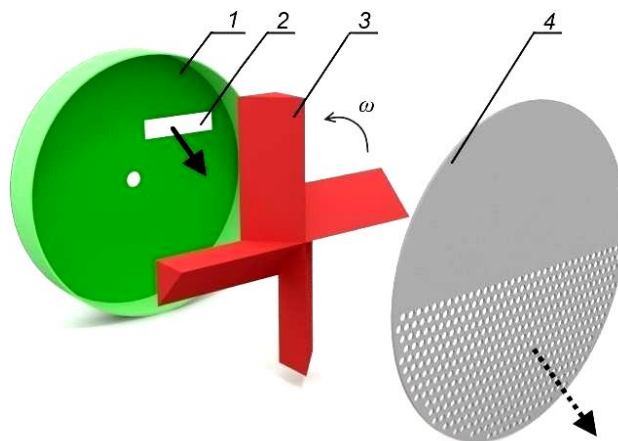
Схема молоткової дробарки ударно-відбивної дії: 1 - корпус робочої камери; 2 - на пластину; 3 - ротор з жорстко установленими билами, ударна поверхня яких розгорнута щодо повздовжньої осі; 4 - торцева стінка з решетом; - → подача матеріалу, що подрібнюється матеріалу; - - → вихід подрібненого матеріалу
